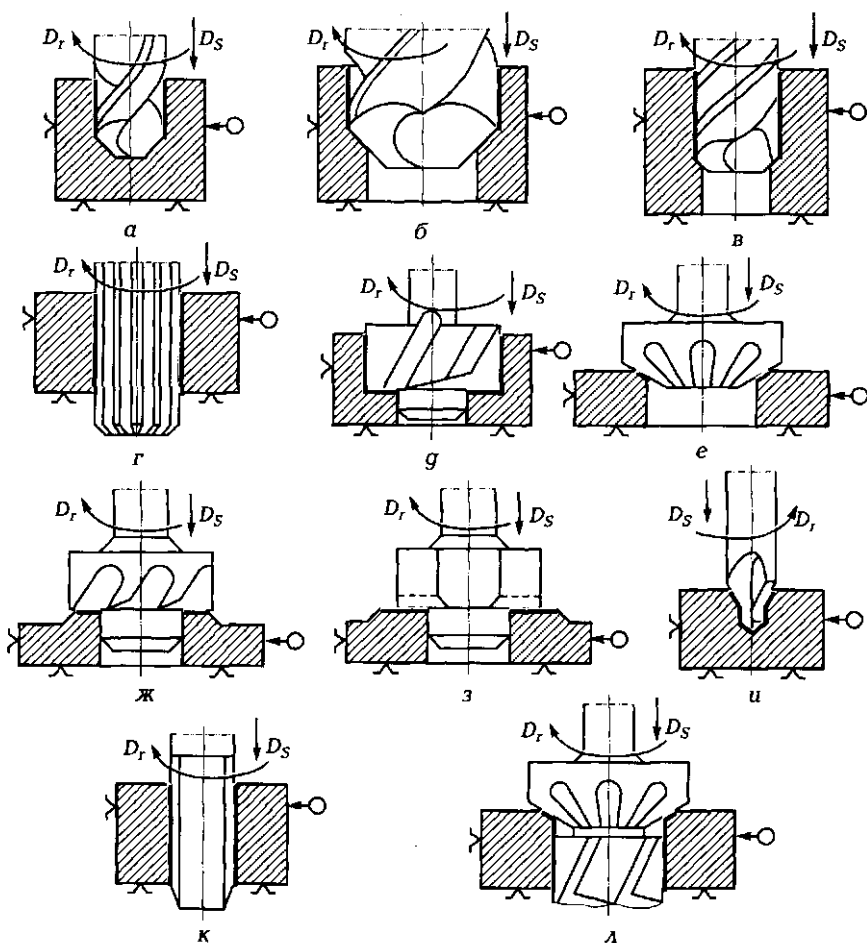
Схемы обработки поверхностей на сверлильных станках:
